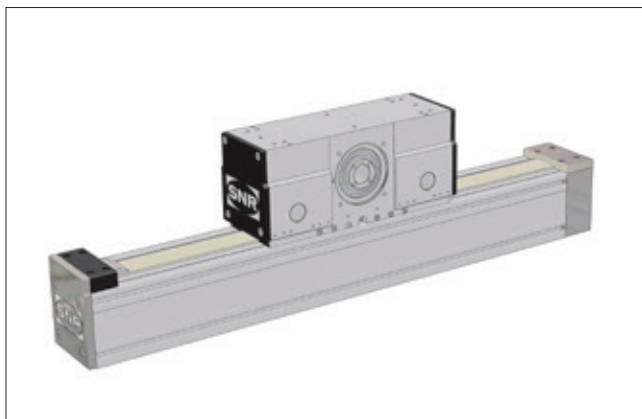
AXC mit Zahnriemen - Ω - Antrieb
